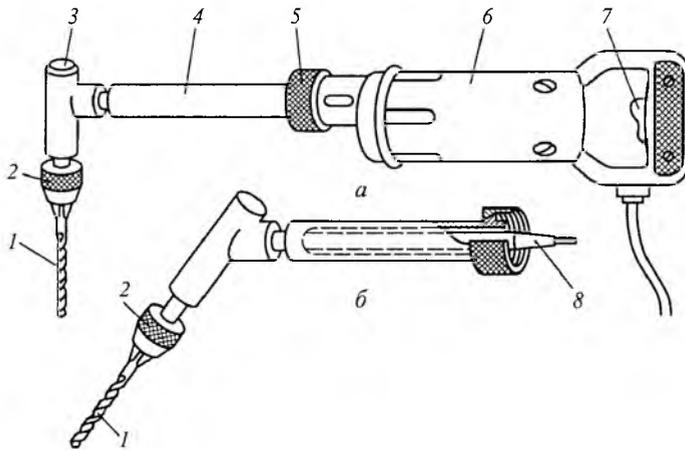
Электрическая сверлильная машина с угловой насадкой: а – машина с головкой 90°; б – машина с головкой 45°; 1 – сверло; 2 – трехкулачковый патрон; 3 – головка; 4 – гайка крепления; 5 – трубка; 6 – корпус; 7 – кнопка выключения; 8 – валик
